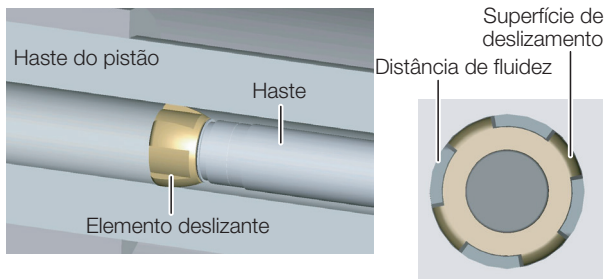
Vista detalhada e superior do elemento deslizante
